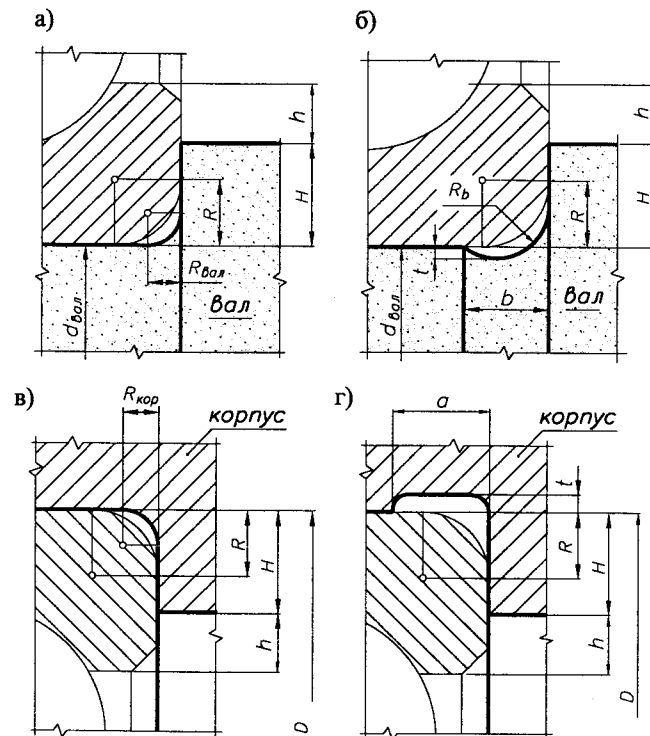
Радиусы закруглений и размеры подточек: а), б) для вала; в), г) для корпуса
